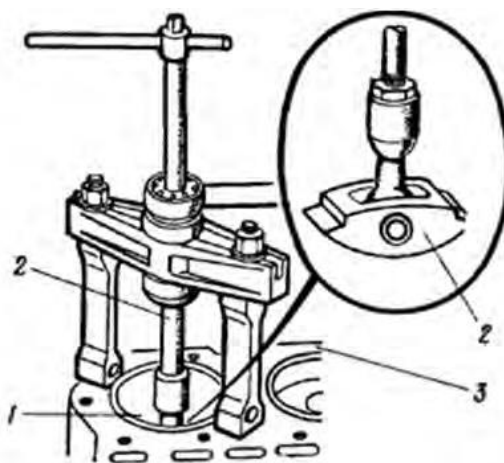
Выпрессовка гильзы из блока цилиндров:
